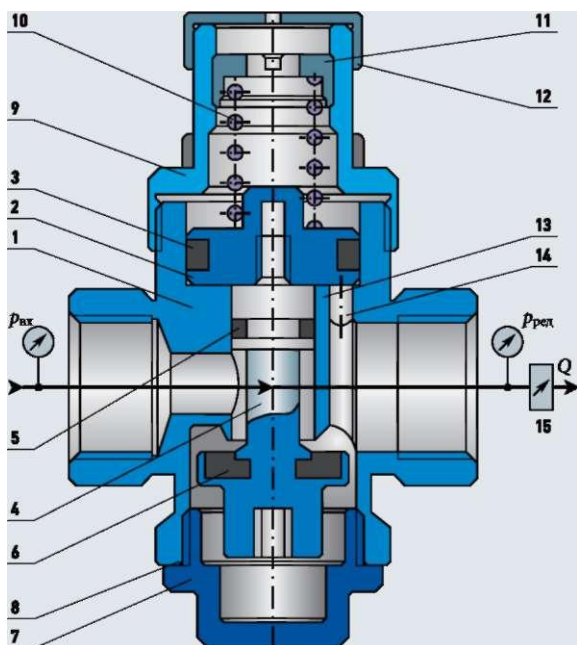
Принципиально-конструктивная схема стандартного поршневого редукционного гидроклапана (1 – корпус; 2 – поршень; 3, 5 – резиновые уплотнительные кольца круглого сечения; 4 – шток с размещенным в его кольцевой канавке резиновым кольцом 5; 6 – завальцованная уплотнительная прокладка; 7 – заглушка; 8 – уплотнительное кольцо круглого сечения; 9 – стакан; 10 – цилиндрическая пружина; 11 – регулировочный винт; 12 – крышка; 13 – седло клапана; 14 – канал, соединяющий подпоршневую полость и полость с редуцируемым давлением $p_{ред}$; 15 – кран в гидравлической линии, по которой вода от редукционного клапана поступает к изливам, сливным устройствам, сеткам и рассекателям водоразборной арматуры)
